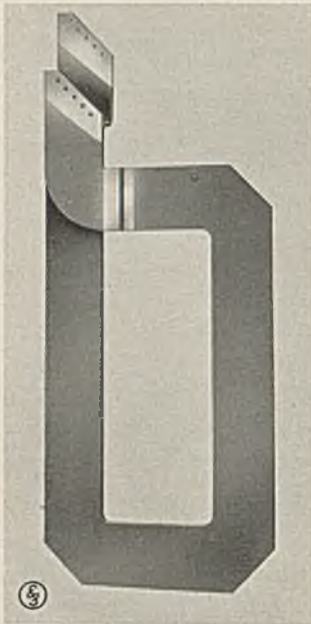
Blechspule für einen Manteltransformator für Ofenzwecke. Die Spule ist aus einer massiven Blechtafel herausgeschnitten.
